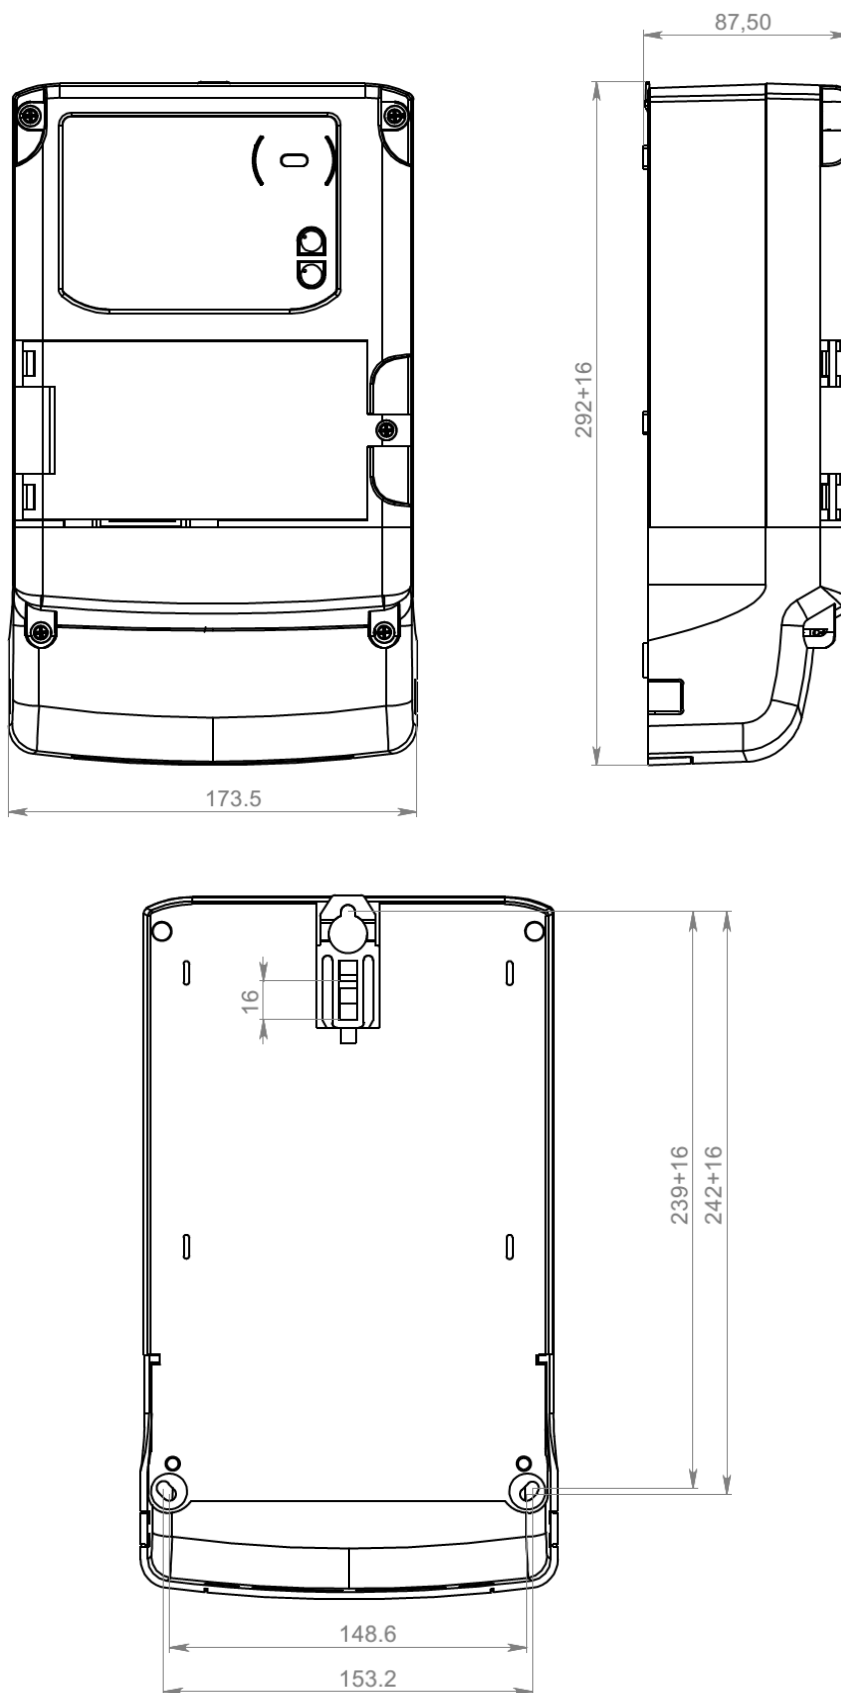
Габаритные и установочные размеры корпуса W32
